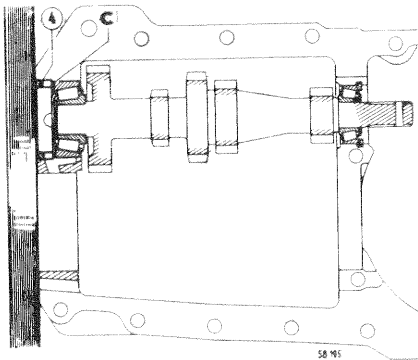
Réglage du roulement arrière de l'arbre primaire
